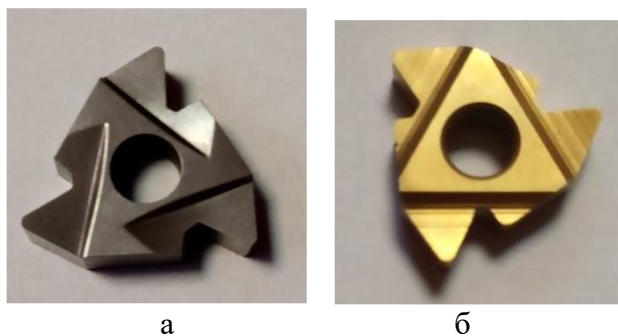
Фото різальних пластин для точіння конічної замкової нарізі з профілем форми Ш:
